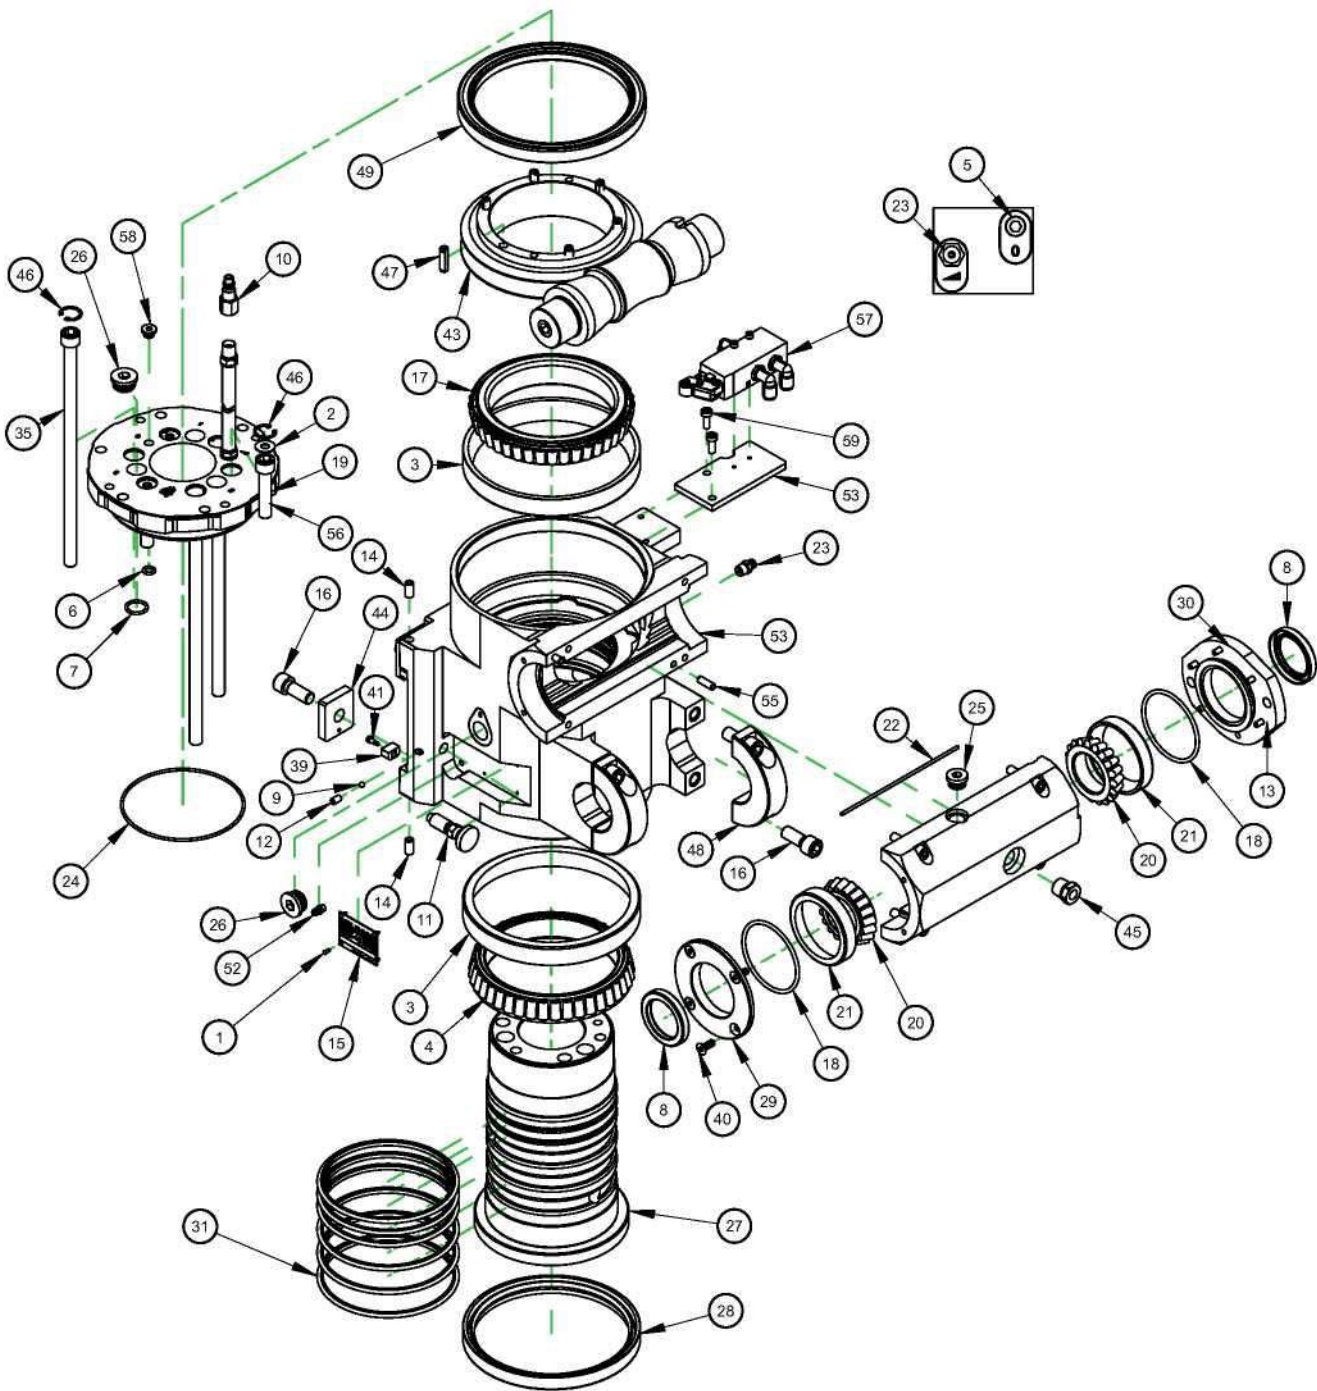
P/N 87913 Baugruppe Hauptkörper FF6300
